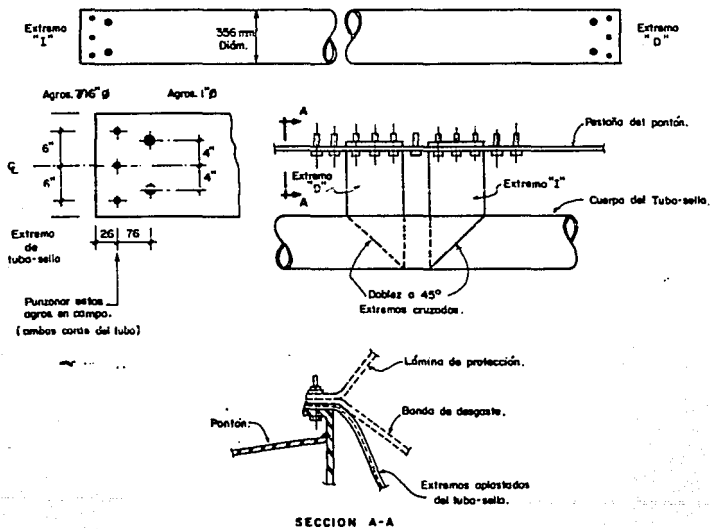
PARTES COMPONENTES DEL TUBO SELLO.
